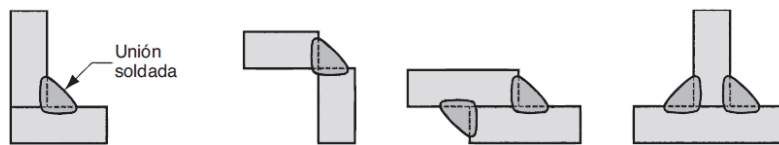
Diversas formas de soldaduras de filete.
